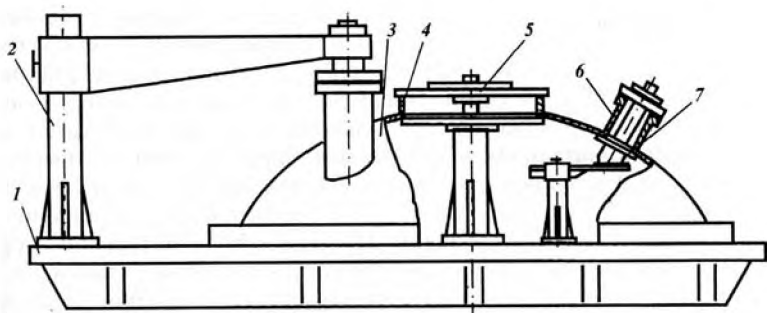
Схема установки фланцев и патрубков на днище на координатной плите: 1 – координатная плита; 2 – стойка приспособления; 3 – днище; 4 – фланец; 5 – приспособление для установки фланца; 6 – патрубок; 7 – приспособление для установки патрубка
